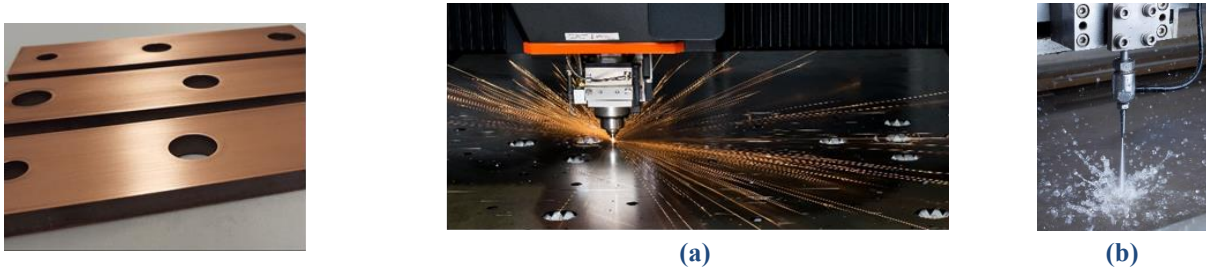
Procédé de fabrication des barres du bobinage massif par découpage laser (a) ou encore par jet d'eau (b).
